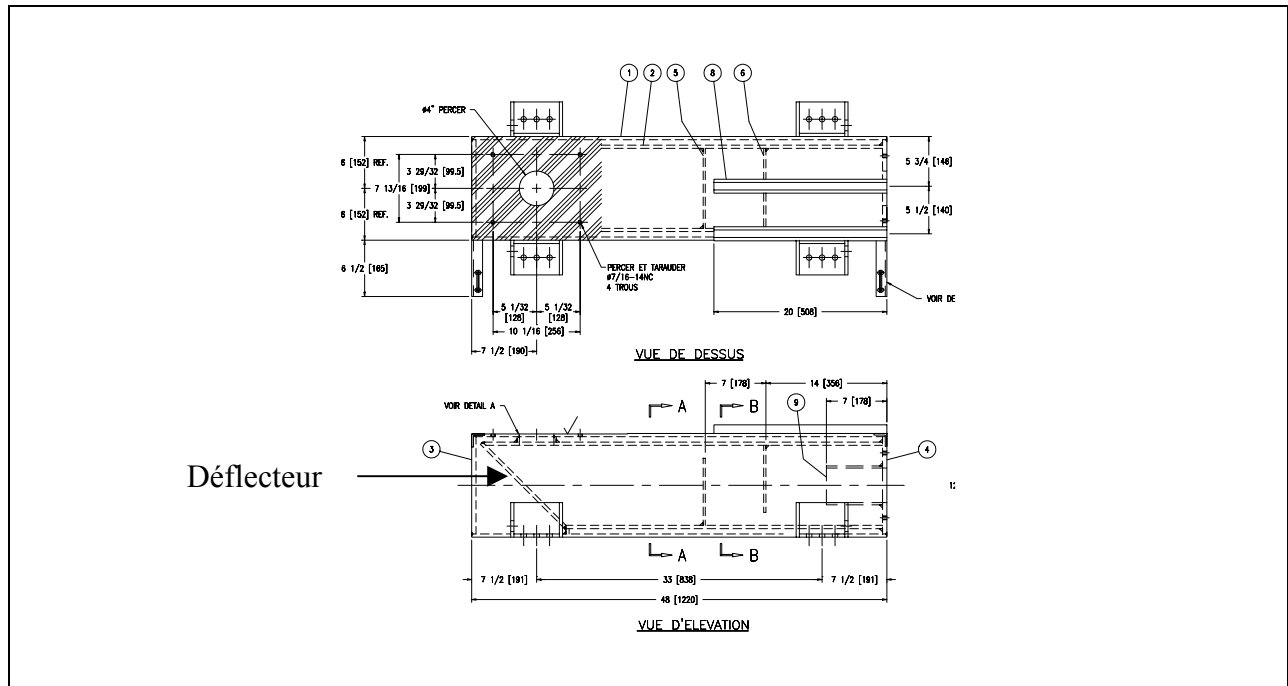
Plan de construction d'une base à déflecteur et double paroi.
